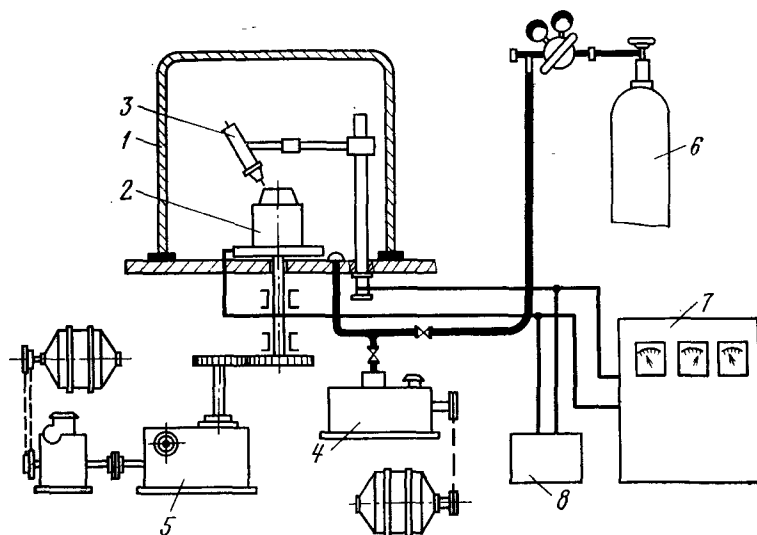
Схема установки для аргодуговой сварки в камере.
